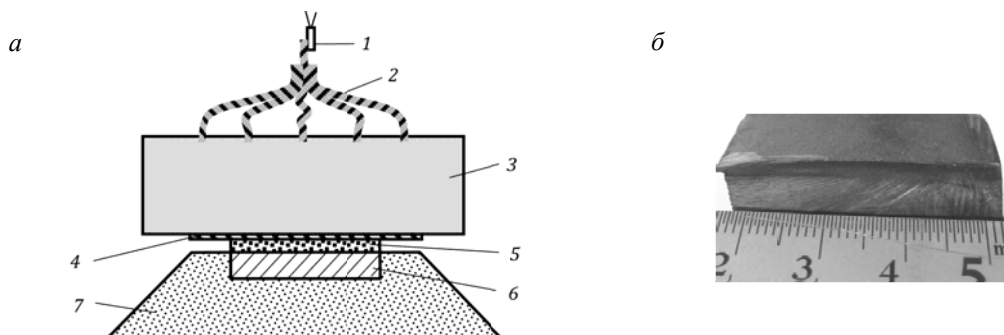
Схема нагружения (а) и внешний вид полученных образцов (б):
